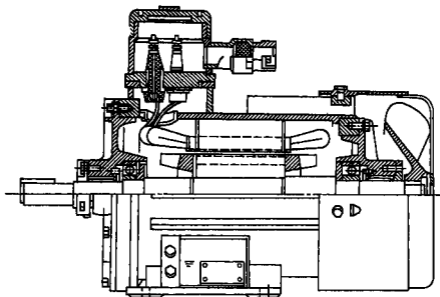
Продольный разрез двигателя ВАО5 для сред 4-й категории
